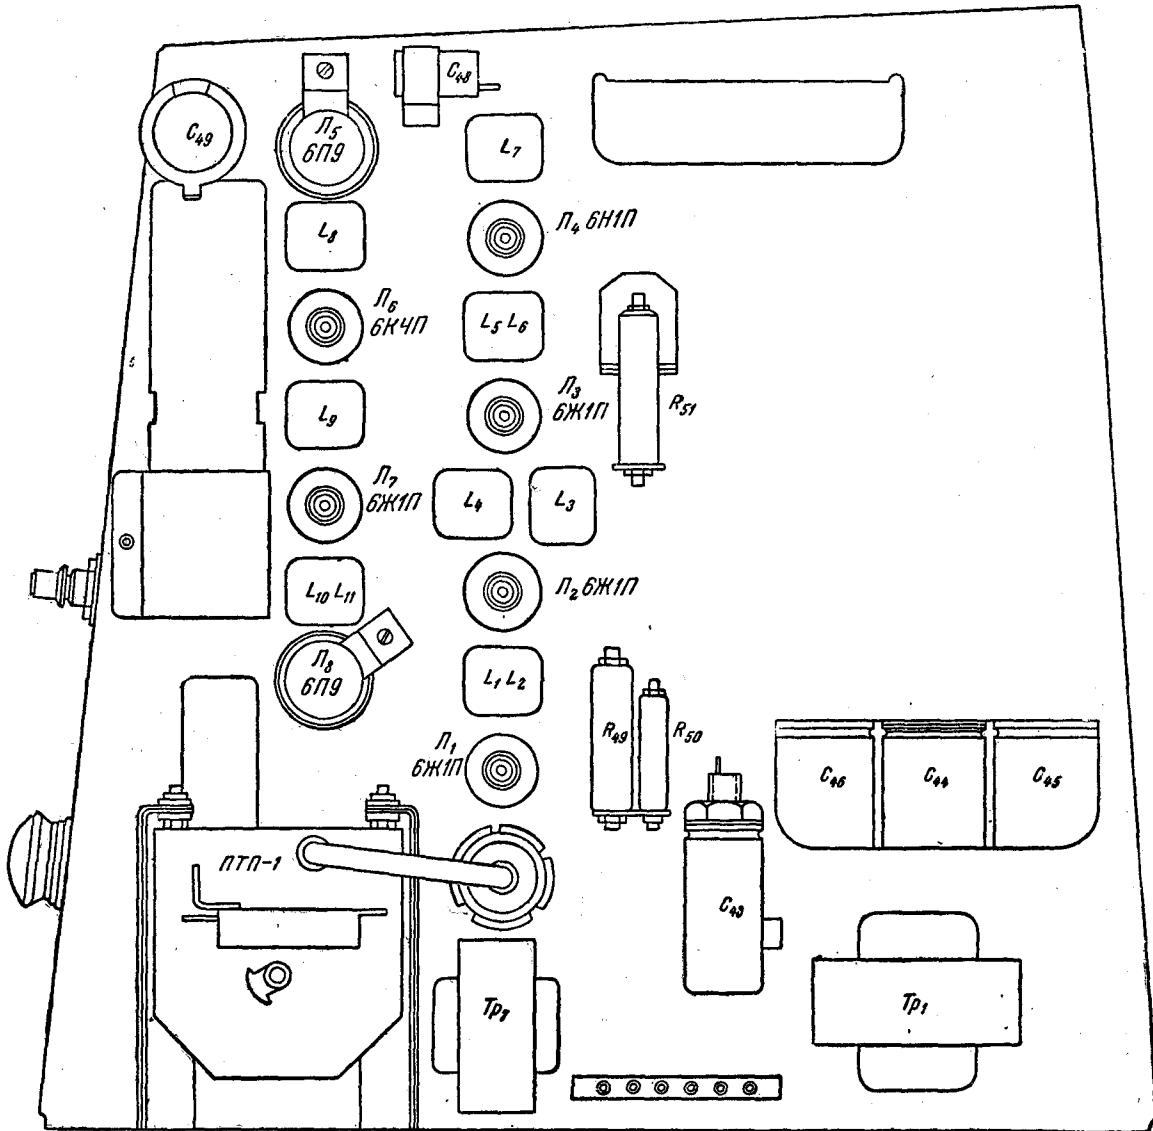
Расположение основных деталей на шасси блока приемников телевизора «Рекорд» (вид со стороны ламп).
